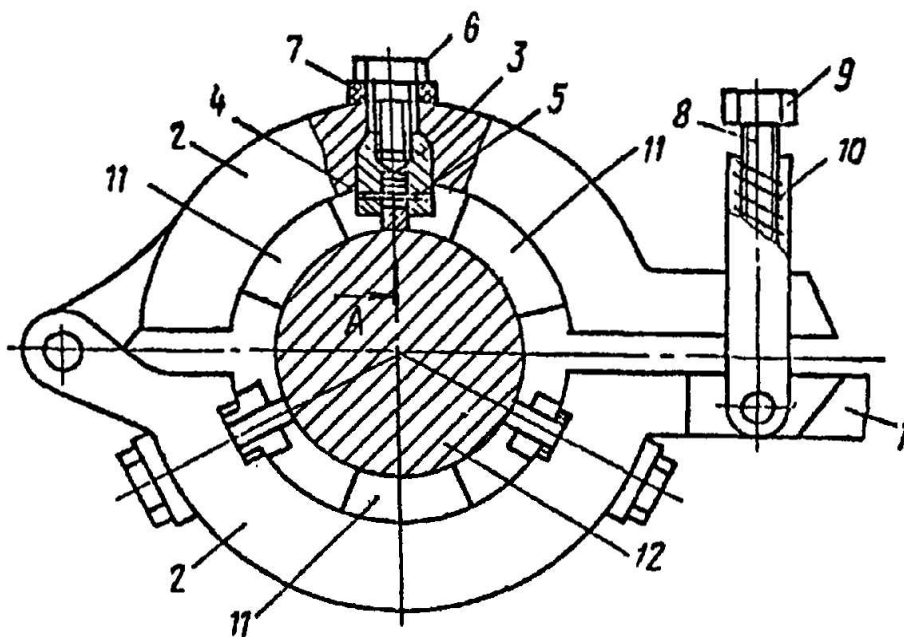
Схема устройства для ФАБО шеек коленчатых валов двигателей
